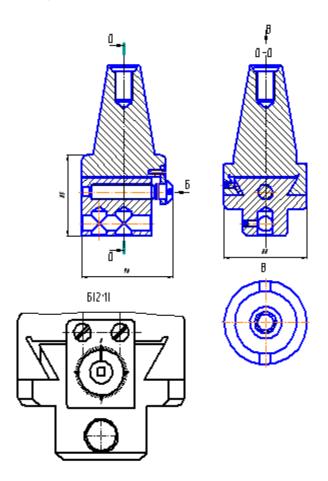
Двухмерный чертеж расточной оправки
